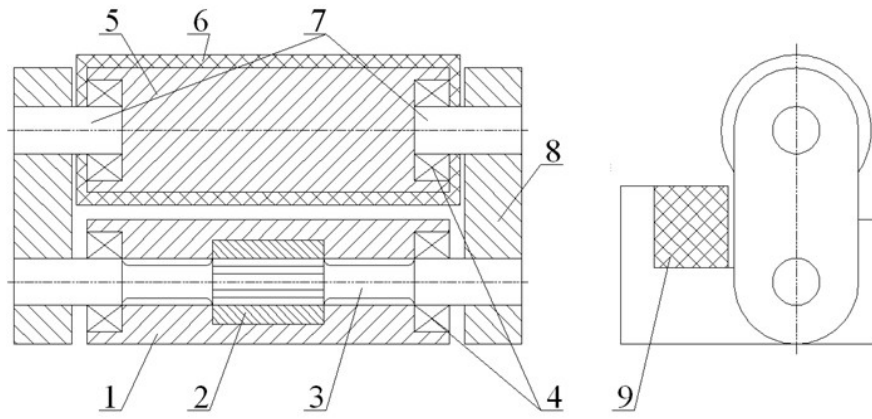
Роликовий вузол стрічкового транспортера: 1 – основа; 2 – шліцьова втулка; 3 – торсіонний вал; 4 – підшипники кочення; 5 – ролик; 6 – армований гумовий чохол; 7 – вісь ролика; 8 – стойка; 9 – гумовий амортизатор.
